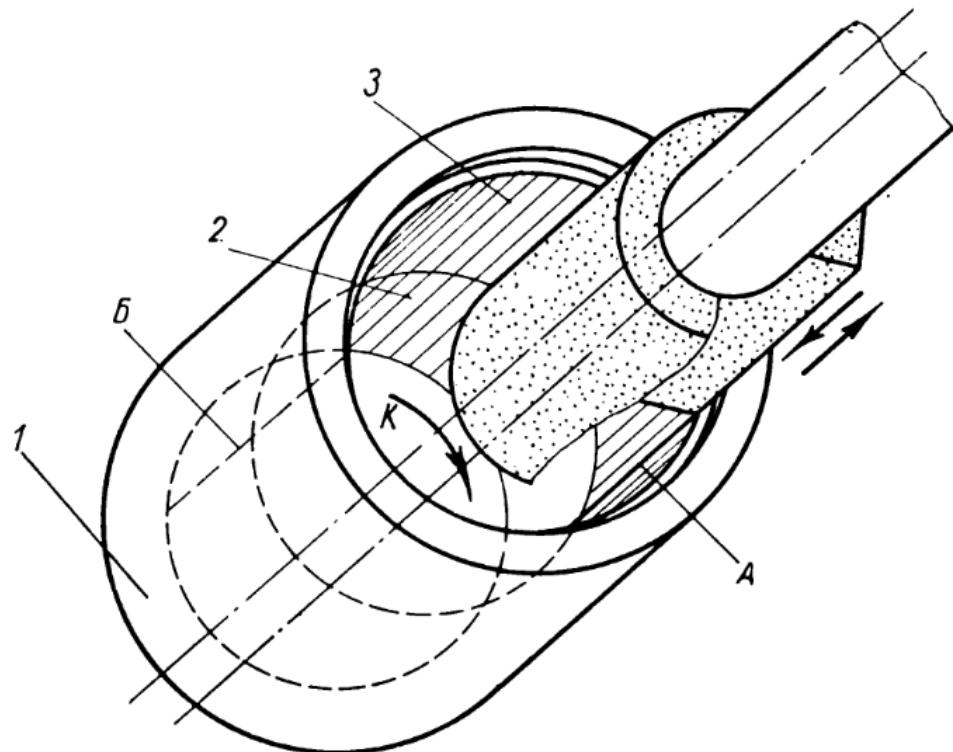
Схема выверки высоты центров осей шпинделя шлифовального круга и обрабатываемой детали
